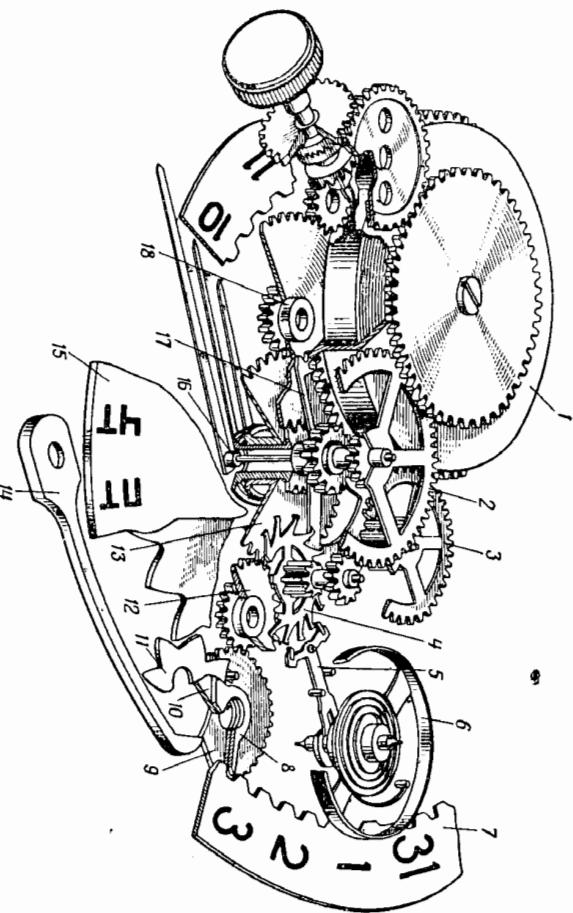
Кинематическая схема часов «Ракета» 2628:
